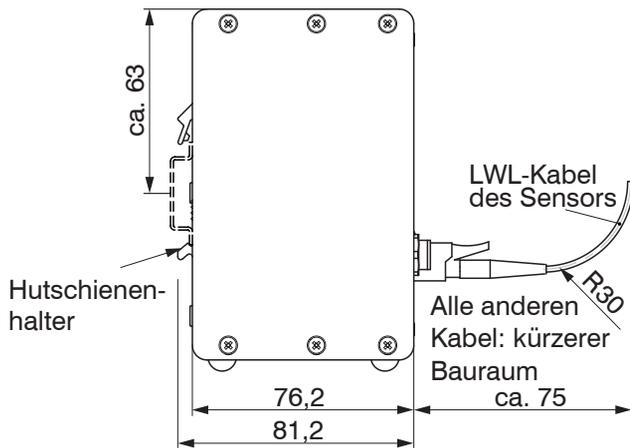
Maßzeichnung Seitenansicht des Controllers IMC5x00, Abmessungen in mm
